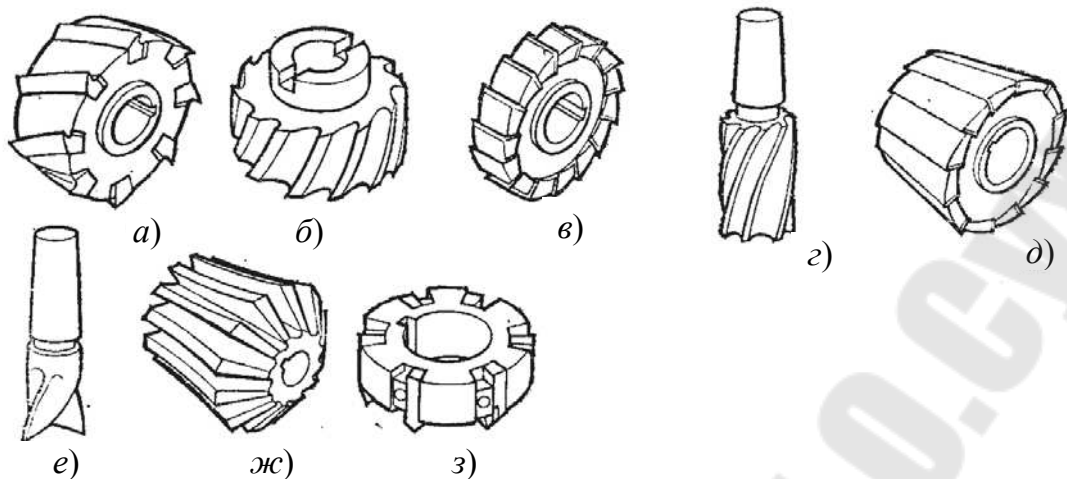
Фрезы для обработки поверхностей на фрезерных станках:
